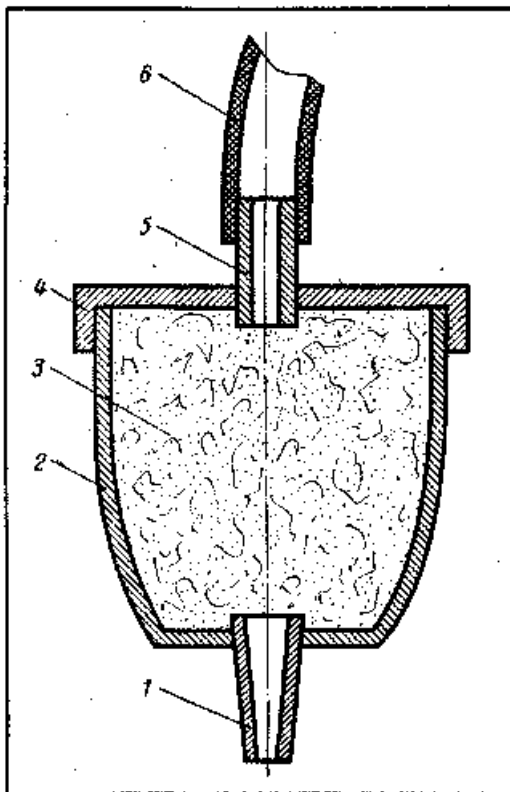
Фильтр-насадка на водопроводный кран: 1 — нижний патрубок; 2 — корпус фильтра; 3 — фильтрующий элемент из капрона; 4 — крышка корпуса (на резьбе); 5 — верхний патрубок; 6 — отрезок резиновой трубки, вставляемый в водопроводный кран
